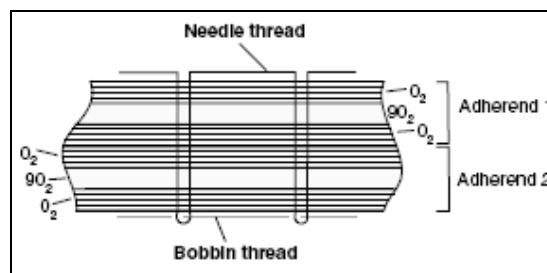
Coupe transversale d'une liaison "lap -joint" avec piquage
